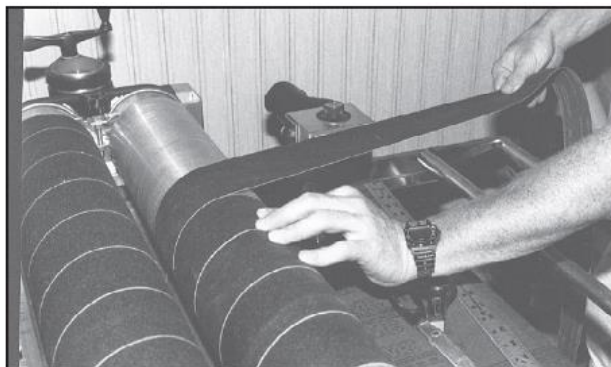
Е Оберните ленту вокруг барабана без перекрытия.
